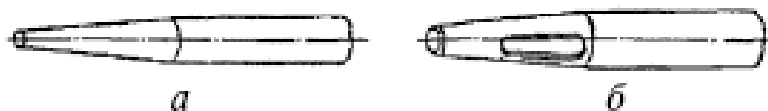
Пробойник: а – сплошной для металлического листа; б – пустотелый для кожи и пластмасс
